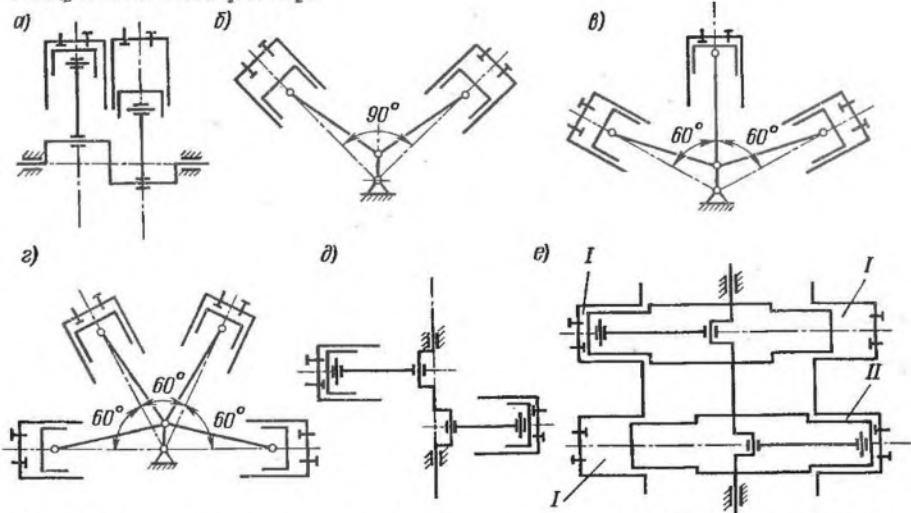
Схемы исполнения компрессоров, унифицированных по цилиндрам: а — вертикальный с числом цилиндров 2; б — У-образный с числом цилиндров 2, 4, 6; в — Ш-образный с числом цилиндров 3 и 6; г — Х-образный с числом цилиндров 4 и 8; д — оппозитный с числом цилиндров 2, 4, 6, 8; е — оппозитный двухрядный с числом цилиндров в первой ступени — 3; во второй ступени — 1 и обводным крещкопфом при $D_I = D_{II}$ (I, II — порядковые номера ступеней сжатия).
